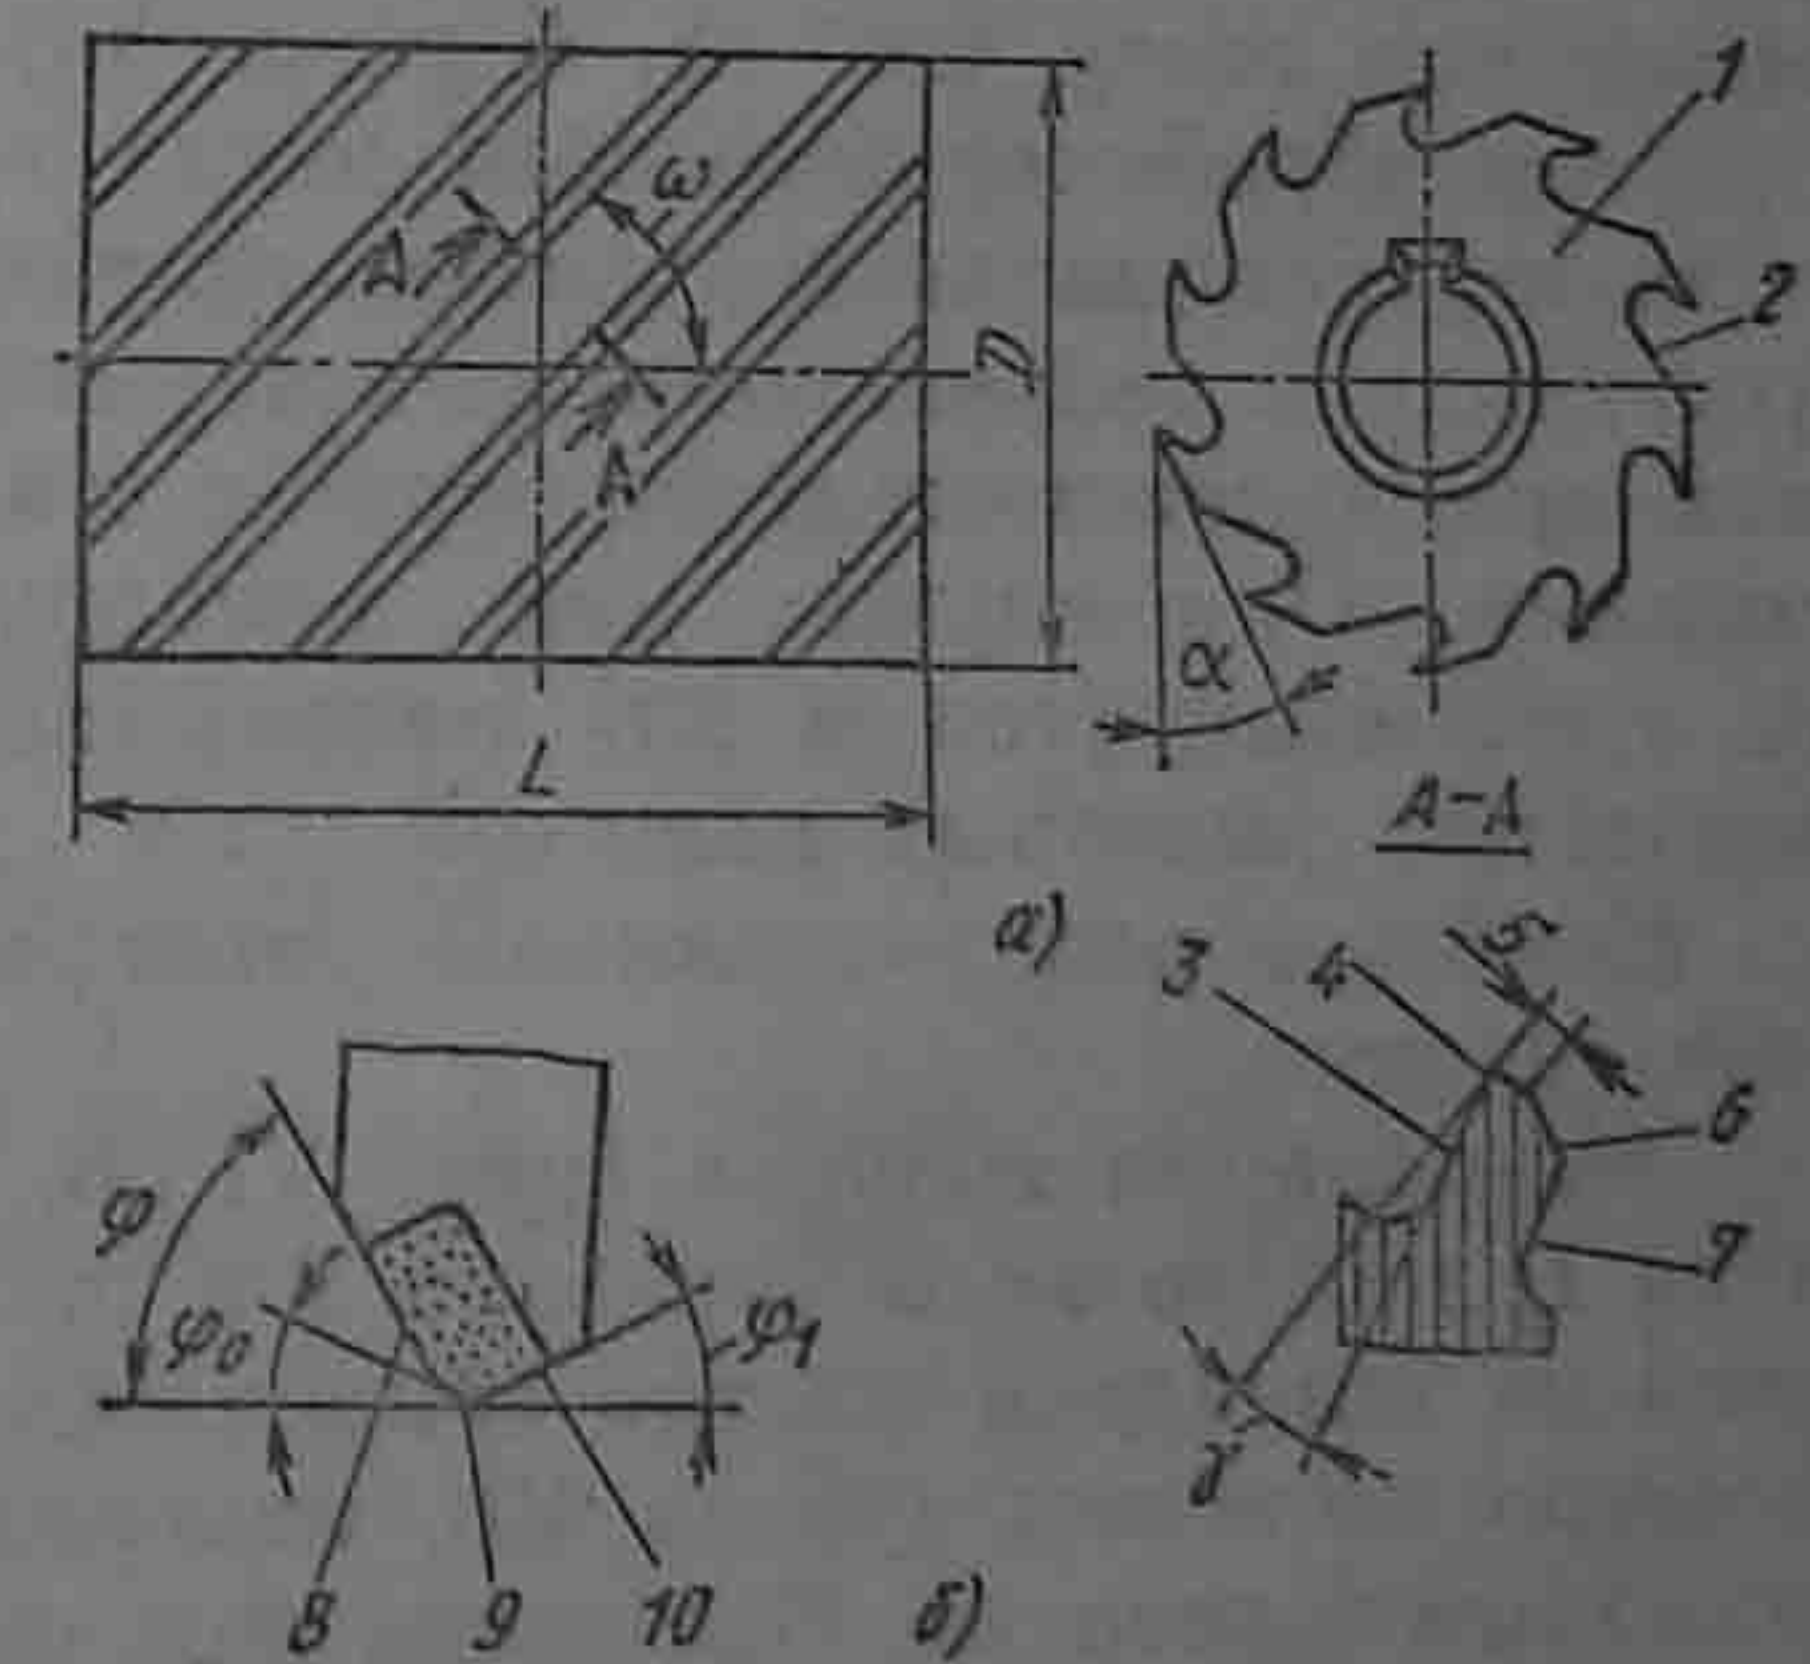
Элементы и геометрия фрезы: D — диаметр фрезы; L — ширина фрезы
